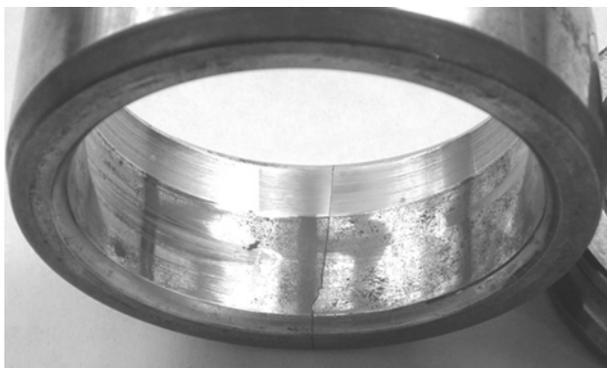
Цвета побежалости на посадочной поверхности внутреннего кольца роликоподшипника, проворачивающегося на валу
